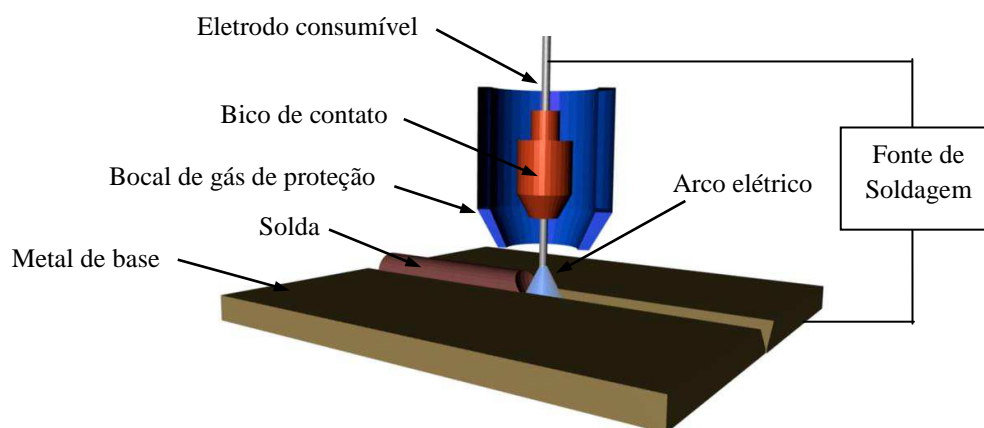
Soldagem com arame sólido sob proteção gasosa (Representação esquemática) [30]
